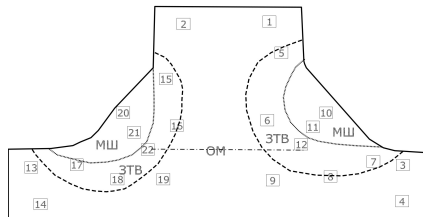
Схема замера и значения твёрдости в точках на шлифе из металла угловых швов приварки второй лопасти к телу наконечника сваи (ОМ — основной металл; ЗТВ — зона термического влияния; МШ — металл шва)
